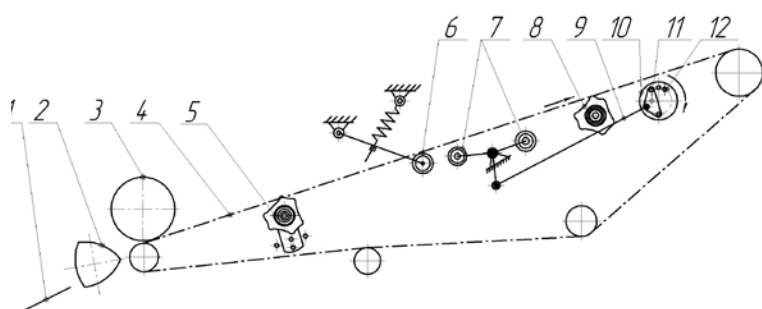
Схема установки встряхивателей и устройства контролирующего величину загрузки сепарирующего элеватора:
